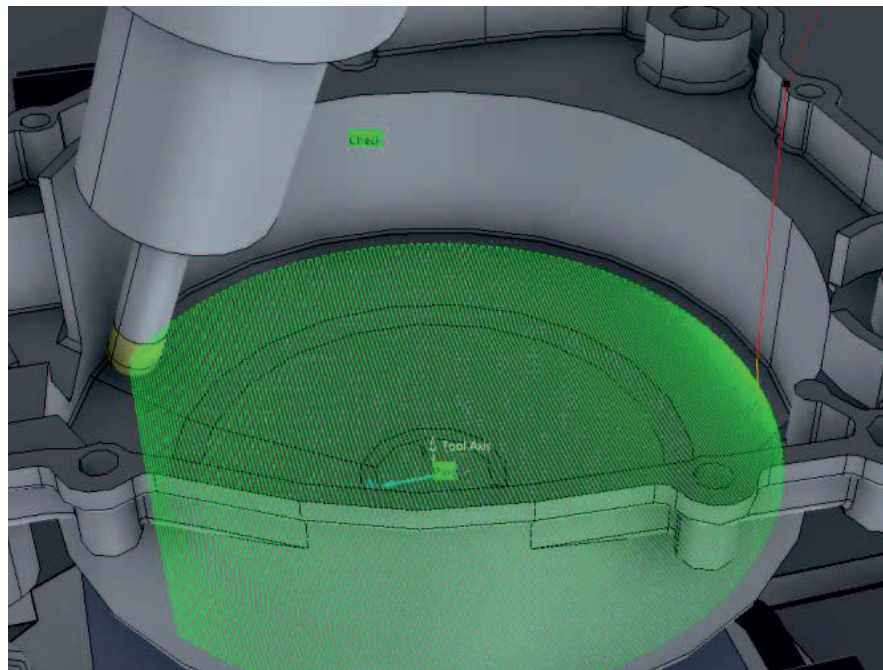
Werkzeugbahnsimulation Kopierfräsen mit angestellter Werkzeugachse
